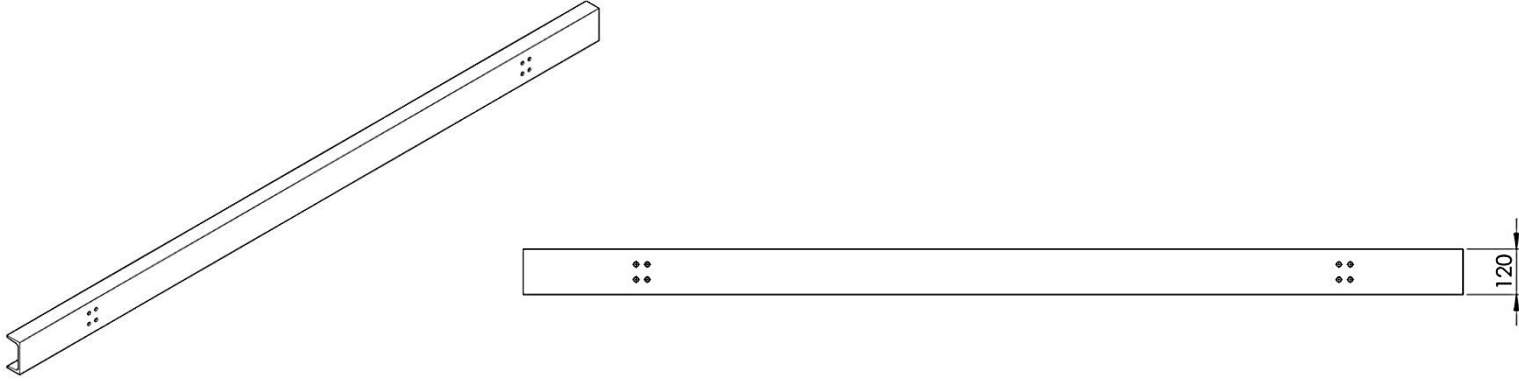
Profiled Walkway Support Kit IPE 240
